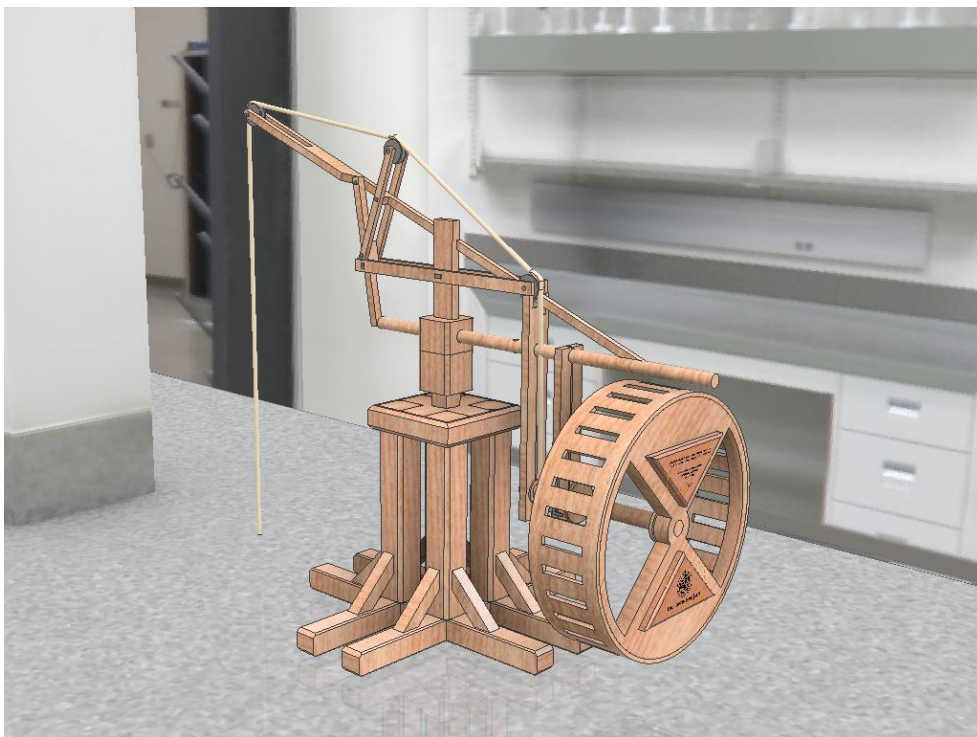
Ensamblaje de Grúa Completa. Fuente: Elaboración propia
